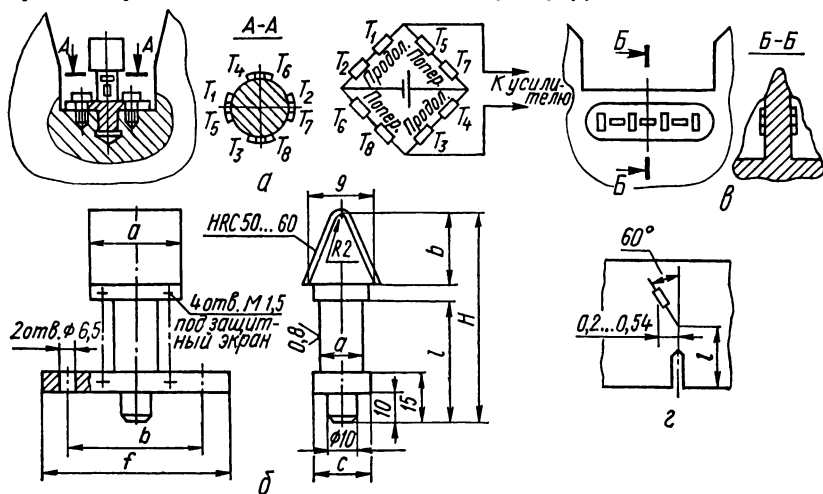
Схема крепления динамометра стержневого типа для испытаний на изгиб и компоновка тензорезисторов (а); некоторые размеры бойка (б); схема расположения тензорезисторов в пазах стандартного диска (в) и на образце (г).
